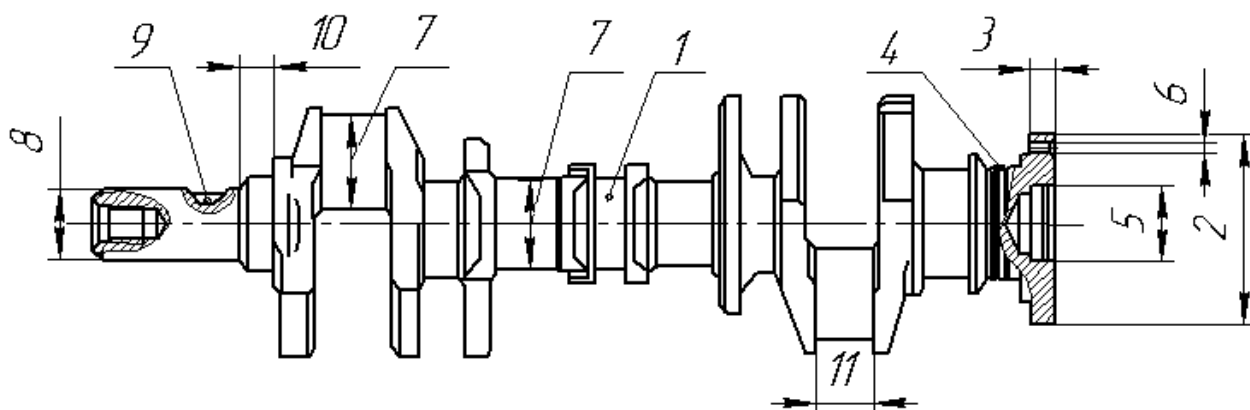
Основные дефекты коленчатого вала на примере двигателя ЗИЛ-130:
